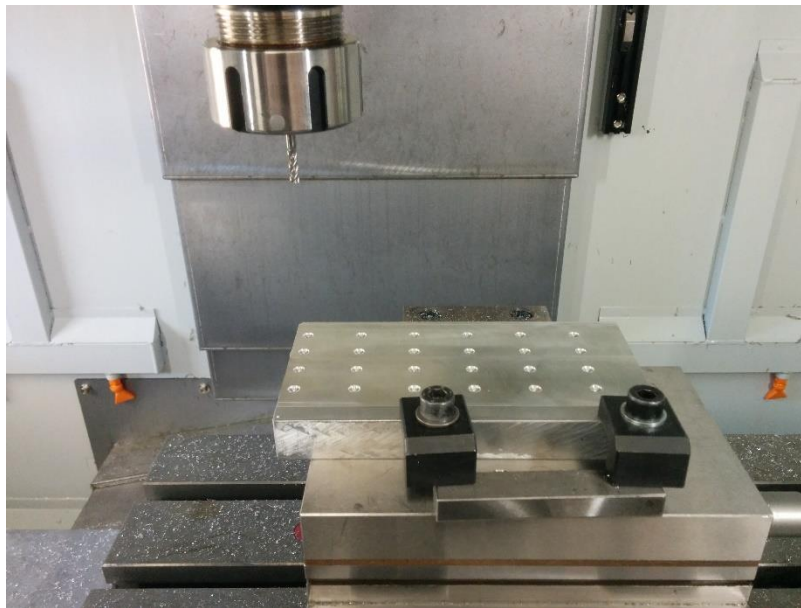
Disposición de pieza y fresa de 4 mm para el ensayo en fresadora Lagun L650, con pasada de planeado ya realizada.
